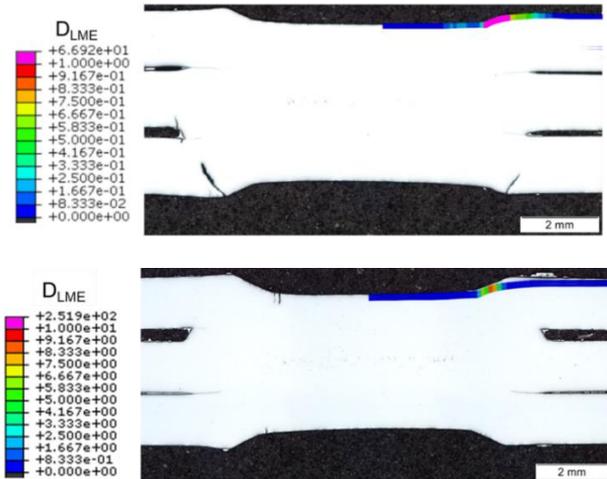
Querschnitt eines Schweißpunkts durchgeführt mit Standardelektrodenkappen (oben) und mit K-Elektrodenkappen (unten); Im Schweißgut sind im oberen Fall deutlich Risse zu erkennen, Bild: MCL
